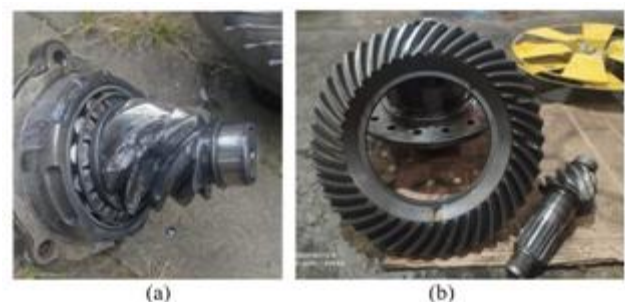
(a) pinion gear (b) ring gear dan pinion gear
